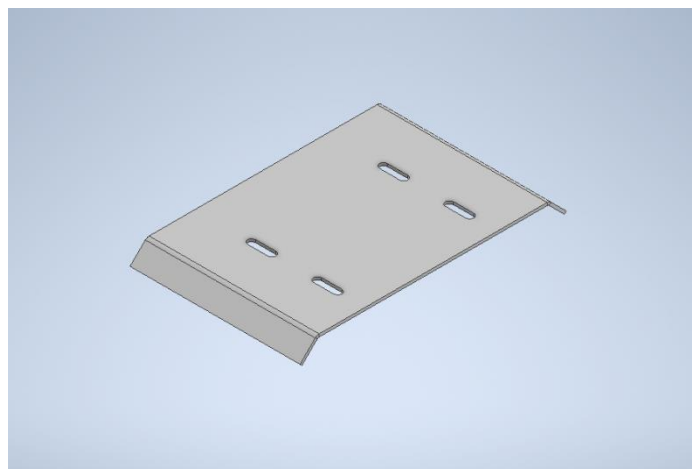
Aplicação Quinadora - Estrado quinado.
